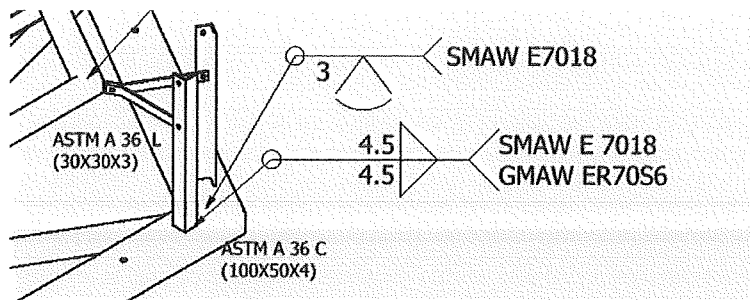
Detalle de Soldadura del soporte de platinas y estructura hexagonal principal.
